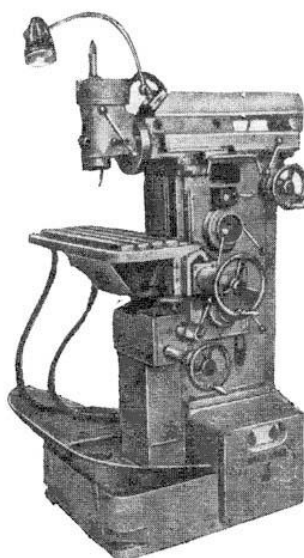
Фрезерный широкоуниверсальный станок 675
